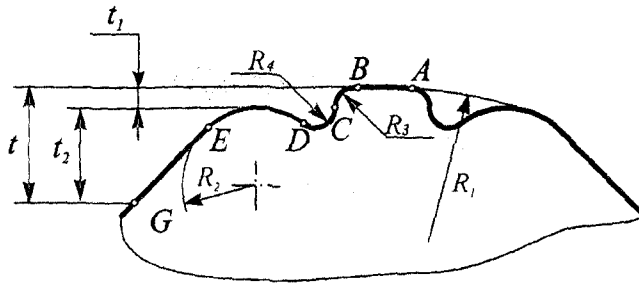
Режущая пластина с двумя ступенями для получистовой и чистовой обработки
